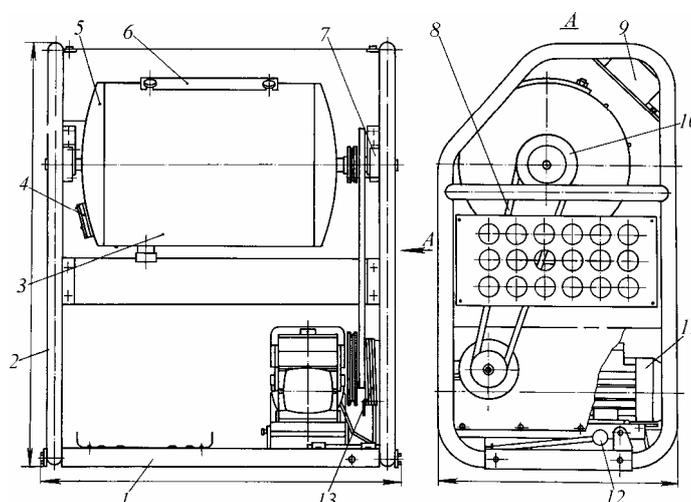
Общий вид маслоизготовителя МИП-1500:
